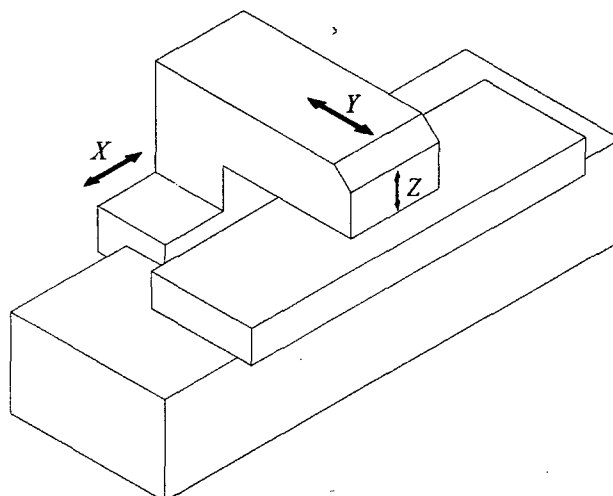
Configuração semelhante a uma punçãoadeira.
